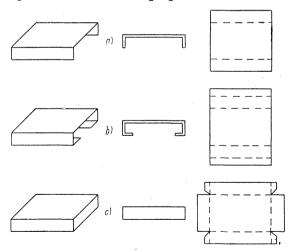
Chassisformen I.a) einfaches U-förmiges Chassis, b) doppelt gebogenes U-förmiges Chassis, c) allseitig abgebogenes kastenförmiges Chassis
